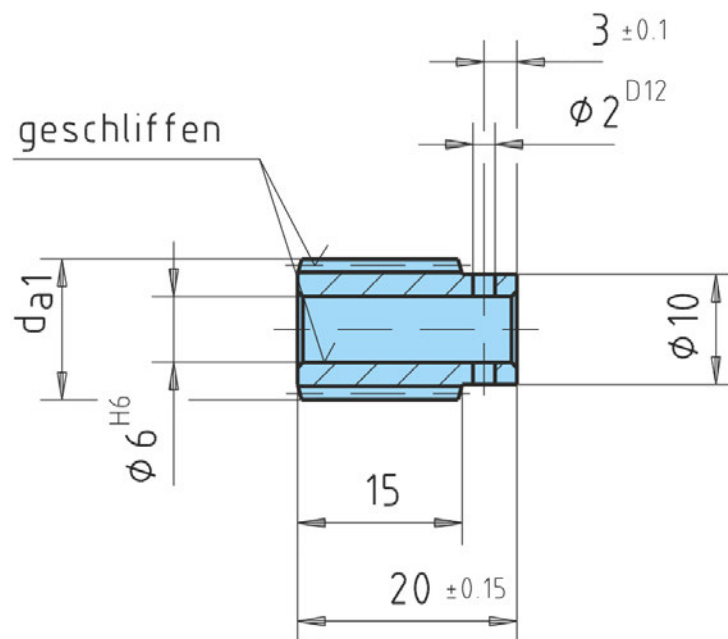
Technische Zeichnung der Schnecke [18]
